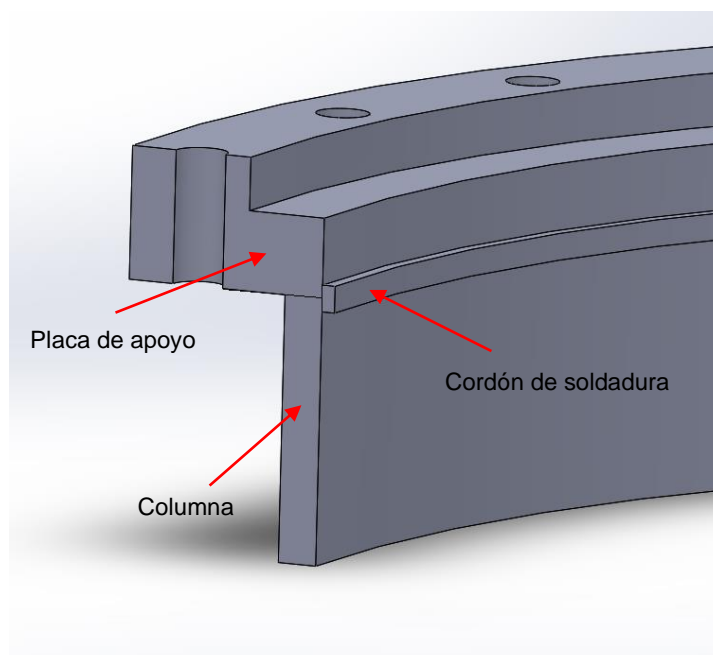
Soldadura de la placa de apoyo del rodamiento.
